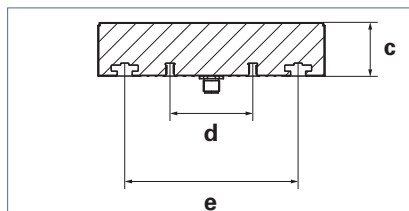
Dimensioni MSAL 90/180 S, sezione trasversale del lato corto dell'apparecchio d'illuminazione.
